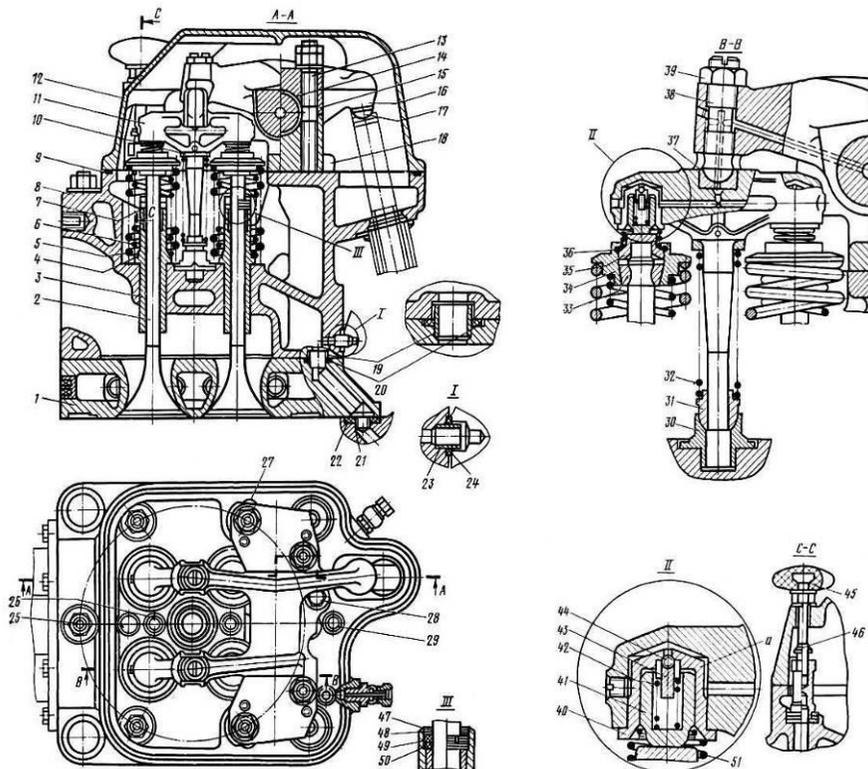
Крышка цилиндра дизеля К6S310DR
